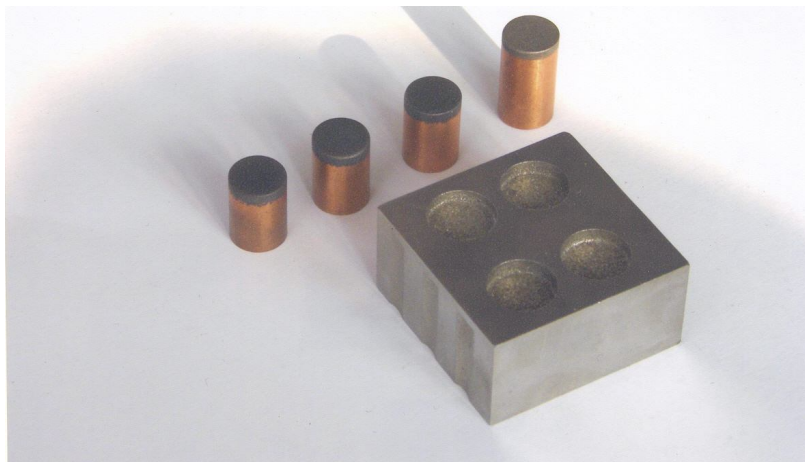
Электроды-инструменты из различных материалов и обработанный образец из закаленной стали ХВГ
